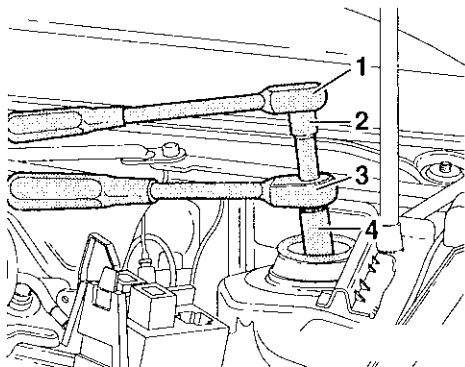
Achterste draag-armlager uit- en inbouwen. Bij inbouwen pijp 3146 gebruiken in plaats van 30-14.
